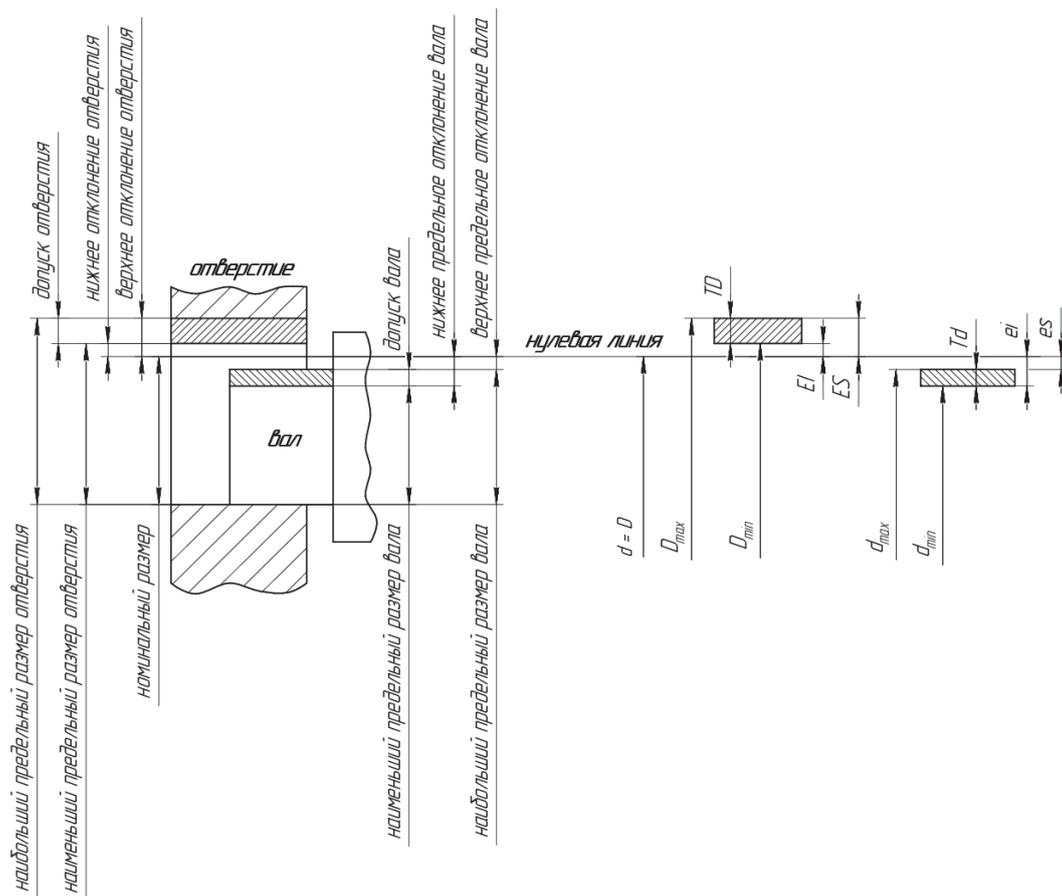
Основные размерные параметры и схема расположения полей допусков
